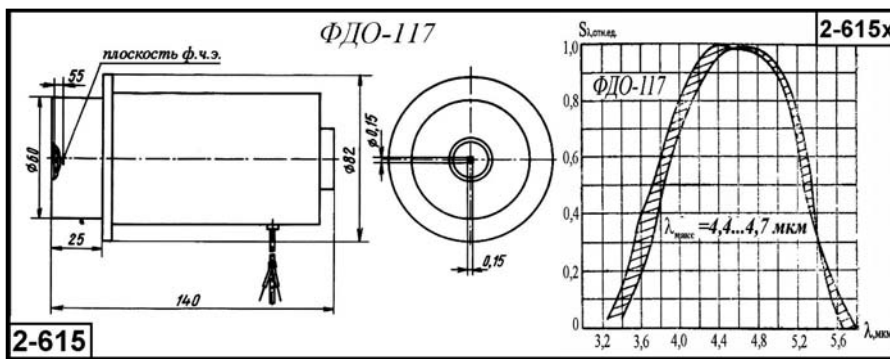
Внешний вид и габаритные размеры охлаждаемого фотодиода ФДО-117
